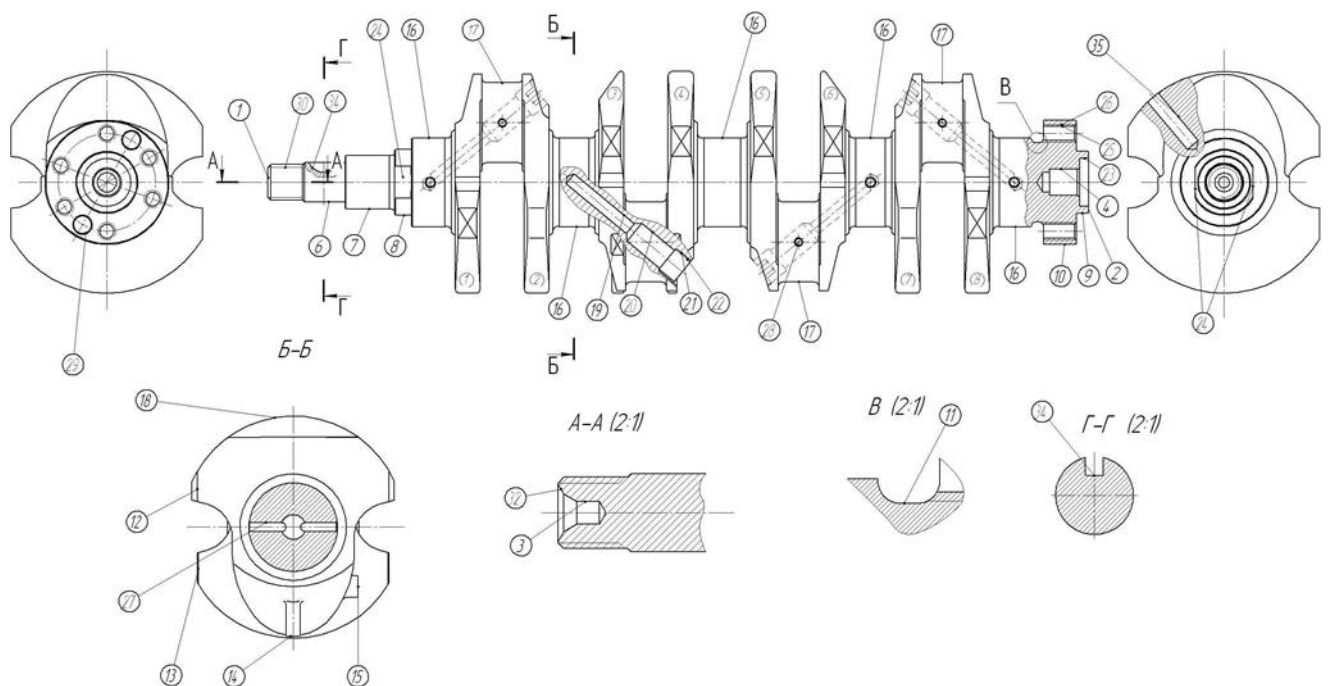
Загальний вигляд деталі з позначеними оброблюваними поверхнями
